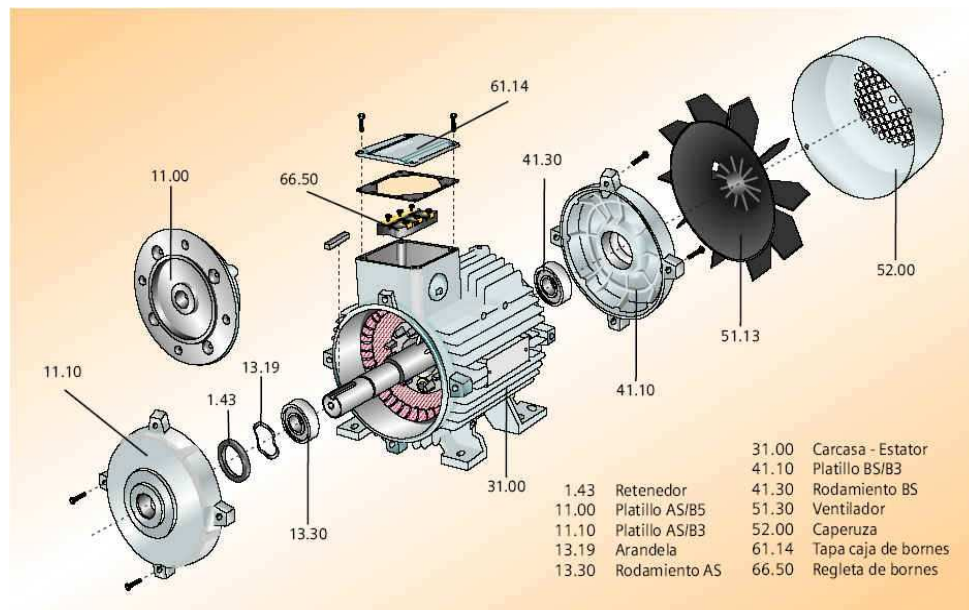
Despiece de un motor de inducción industrial de rotor de jaula de ardilla
